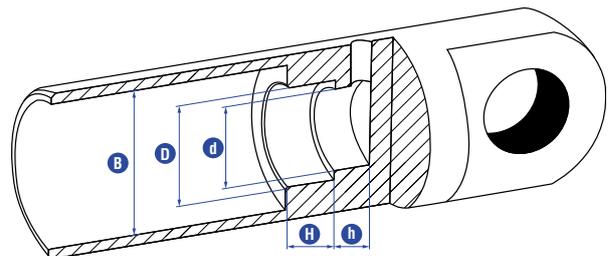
Bauraum Mindestanforderungen für Zylinder
